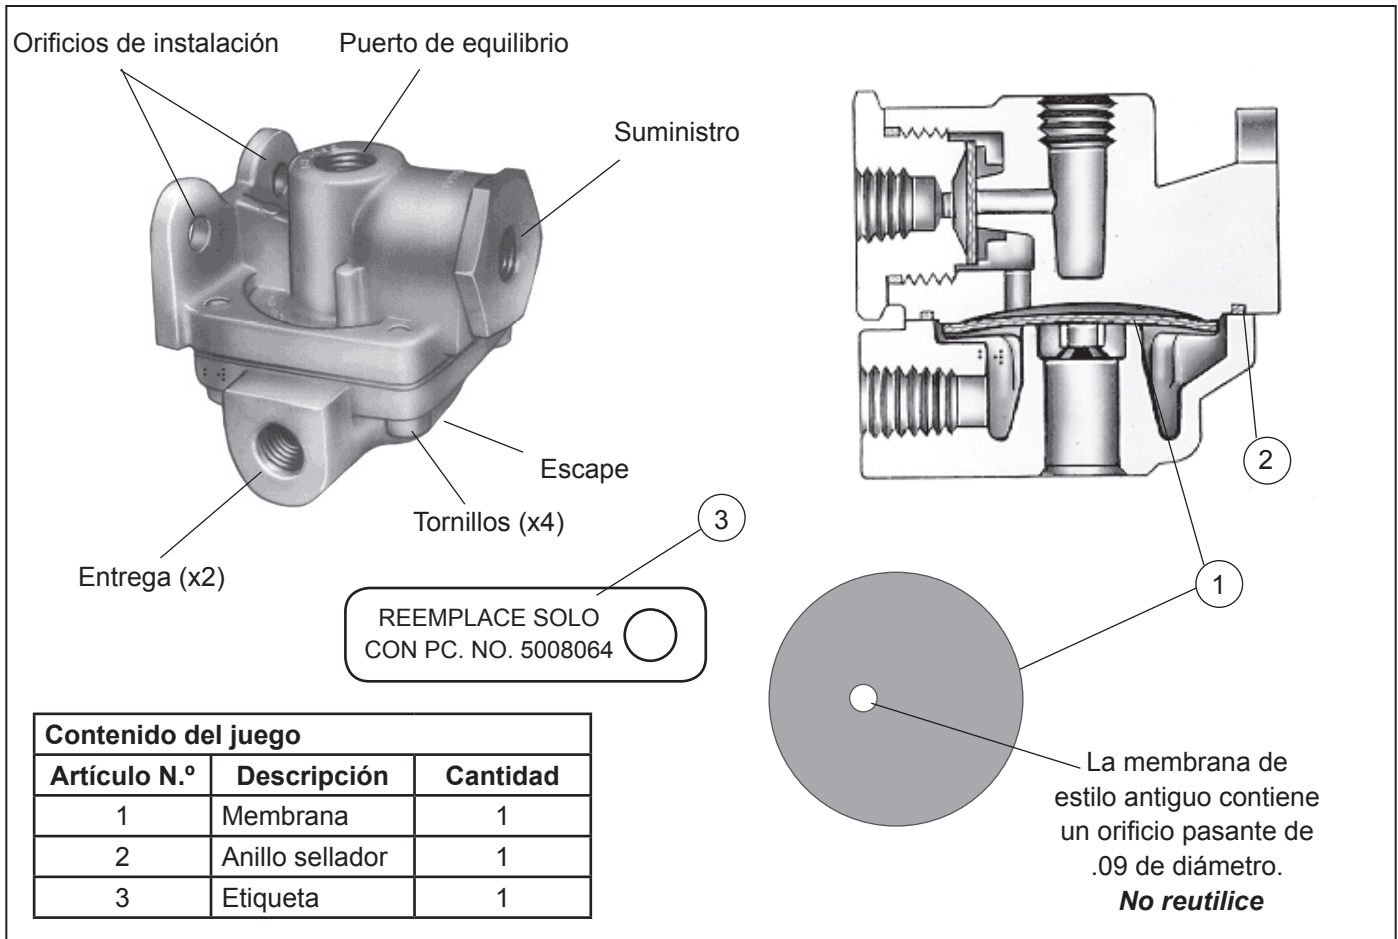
Vista en sección y exterior de la válvula QR-1C® de Bendix®
